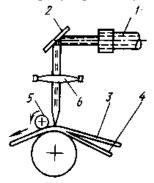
Схема сварки пленки лучом лазера:
